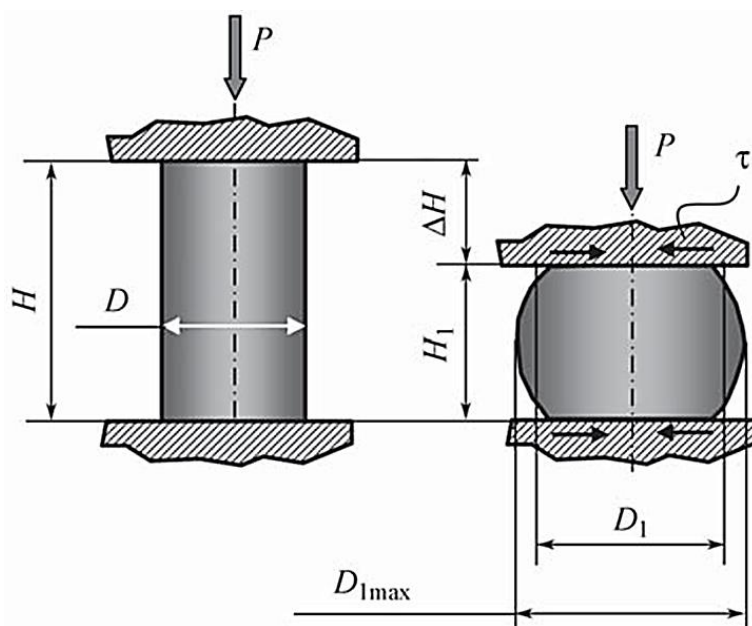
Схема осадки заготовки: P – сила; H и H_1 – высота заготовки соответственно до и после обработки; D – диаметр заготовки до обработки; D_1 – средний диаметр заготовки после обработки; D_{1max} – средний диаметр заготовки после обработки
